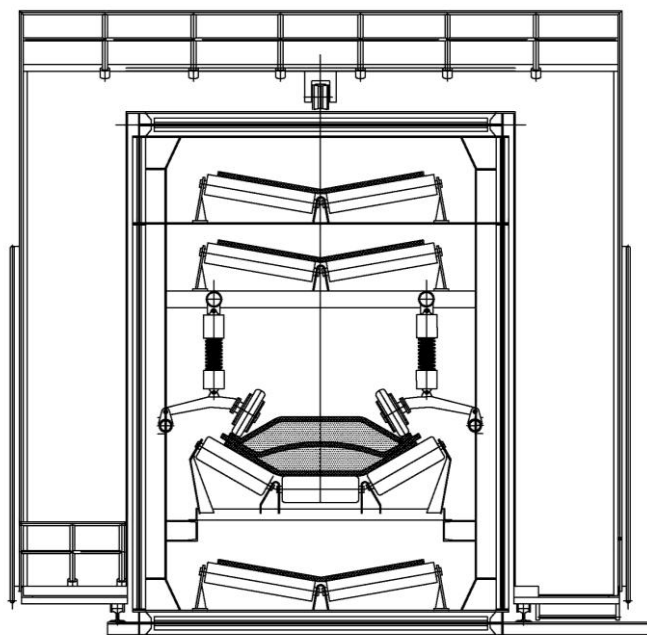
Схема конструкции ленточного конвейера с двумя прижимными лентами
